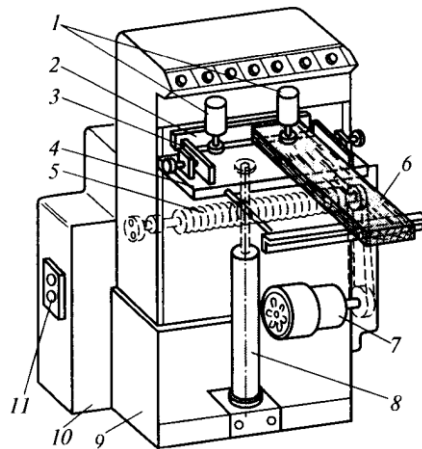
Шипорізний верстат для виробітку прямих ящикових або клинових шипів: 1 – гідропритиски; 2 – торцевий упор; 3 – напрямна лінійка; 4 – піднімальний стіл; 5 – фрезерний вал; 6 – заготовка; 7 – електродвигун; 8 – гідроциліндр; 9 – станина; 10 – гідроагрегат; 11 – рукоятка дроселя
